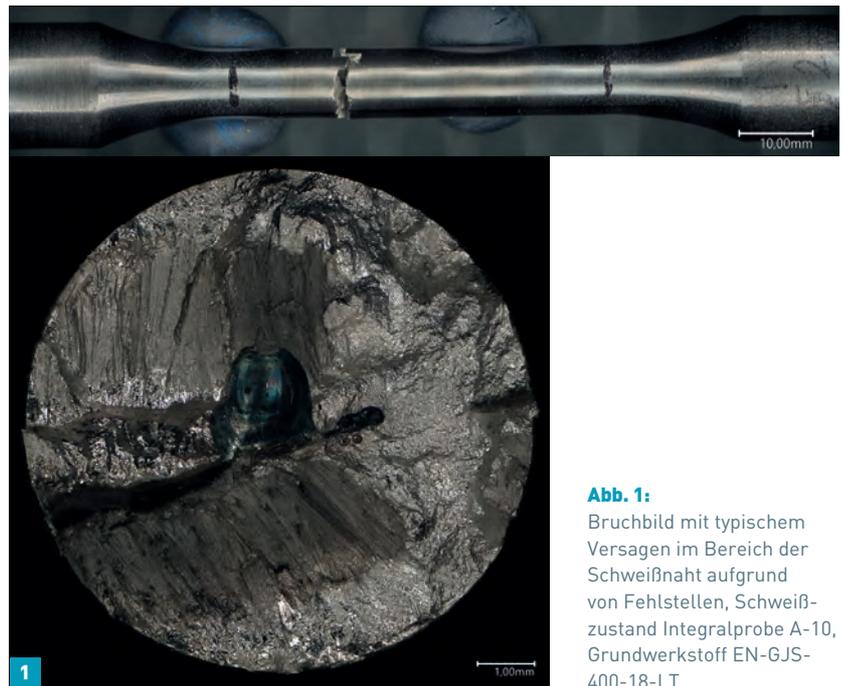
Bruchbild mit typischem Versagen im Bereich der Schweißnaht aufgrund von Fehlstellen, Schweißzustand Integralprobe A-10, Grundwerkstoff EN-GJS-400-18-LT
